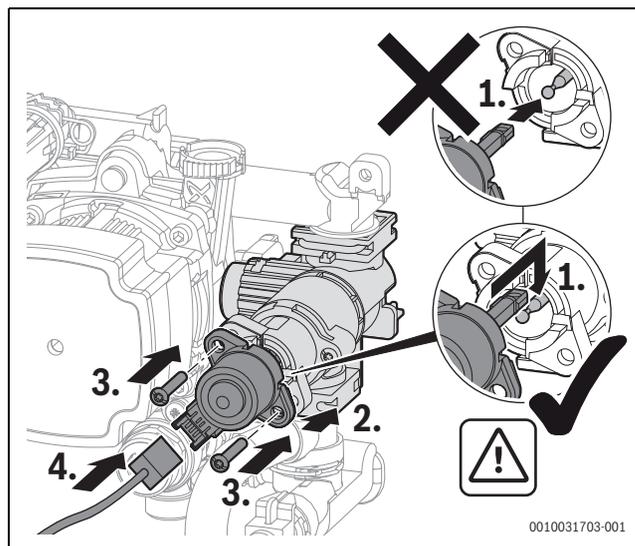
Montare il motore sulla valvola a 3 vie (variante con viti)
